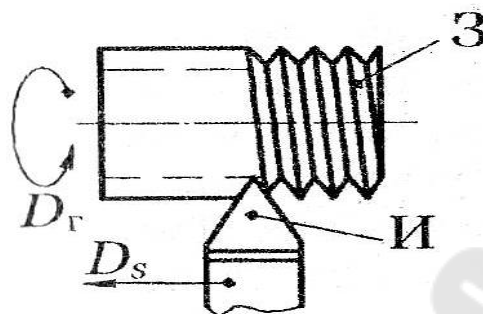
Схема обработки поверхности резанием: И – инструмент, З – заготовка, D_s – движение подачи
